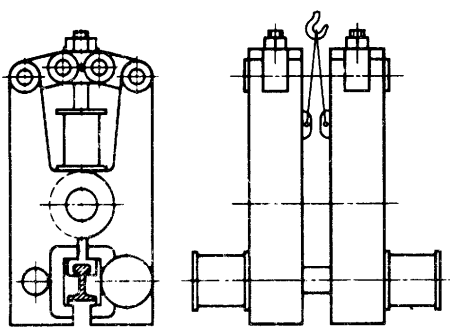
Силовая часть контактной машины для сварки стержней и рельсов
